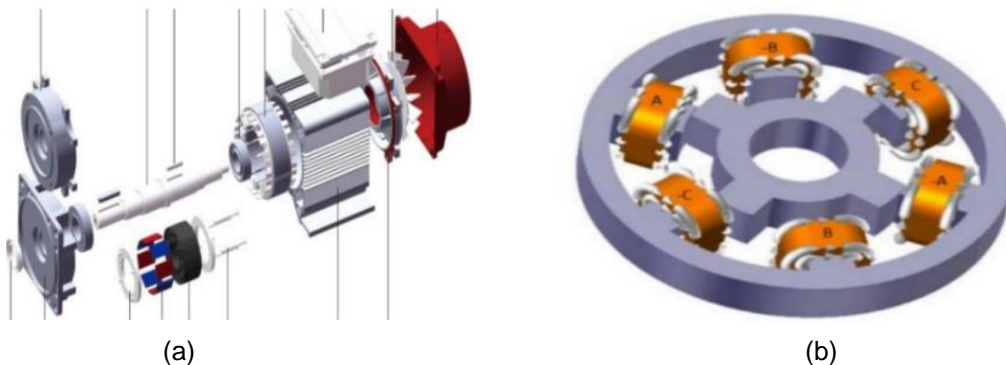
Demonstração das principais partes que compõem um motor CC e a imagem em explosão de um motor assíncrono de indução.
